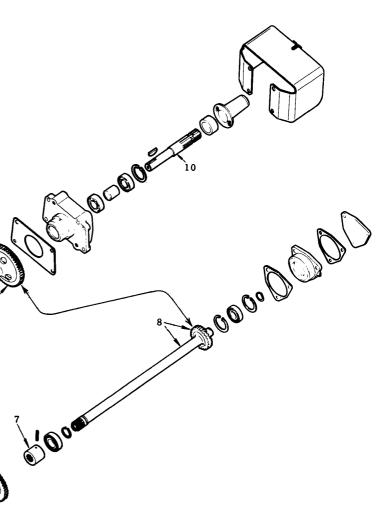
Vue éclatée des prises de force avant et arrière.
